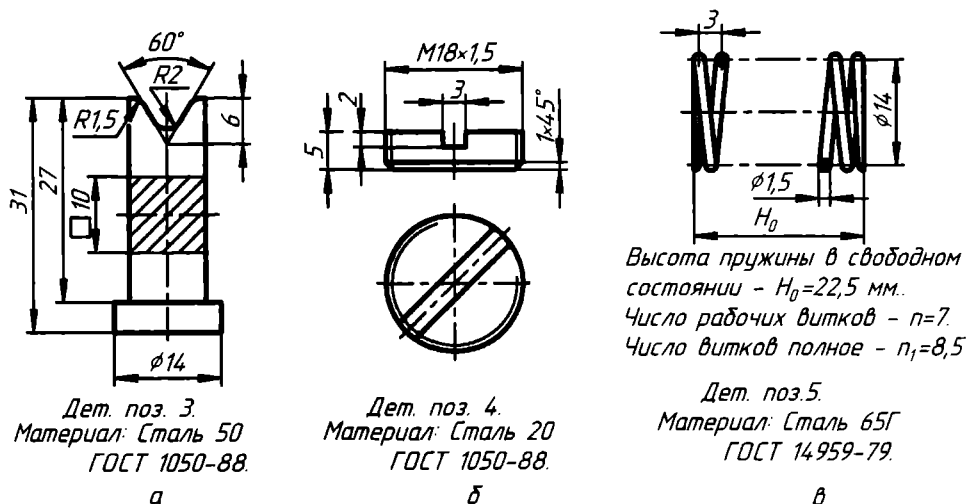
Чертежи: а — выталкивателя; б — пробки; в — пружины
